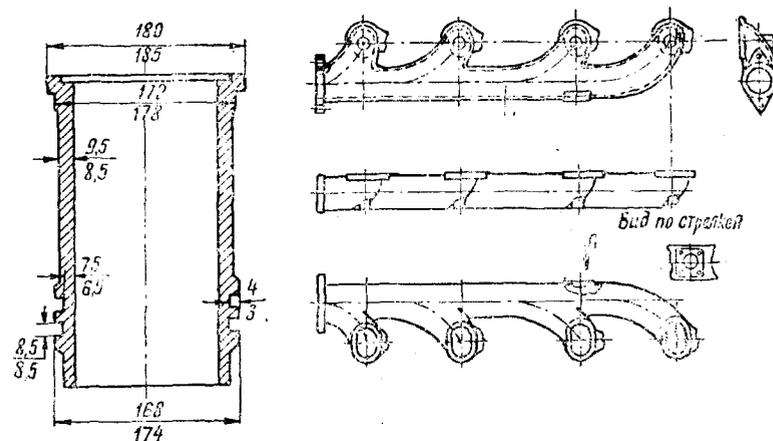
Вставная гильза цилиндра и всасывающая труба двигателя МГ-17
